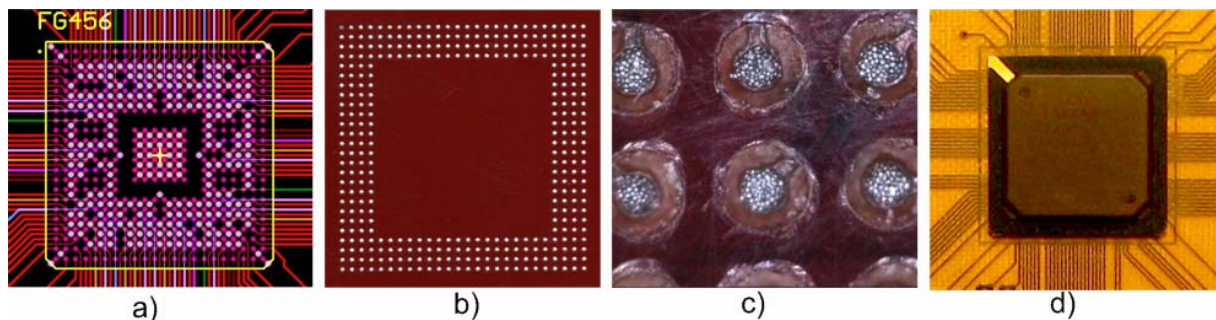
Proceso de montaje de una FPGA Spartan3 con encapsulado BGA de 456pines
